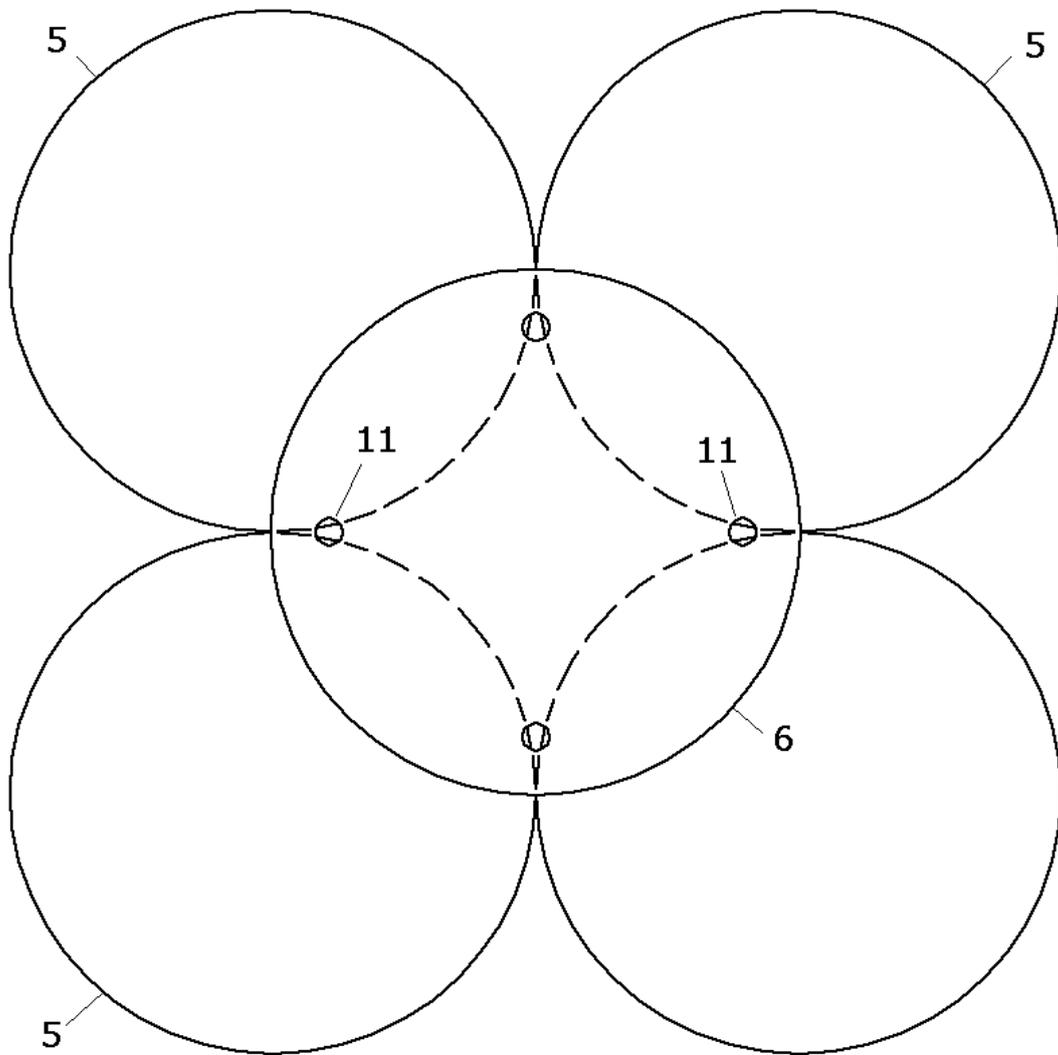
Drehkolbenarray für einen Stirlingmotor mit Druckausgleichsventilen und Stützringen.
